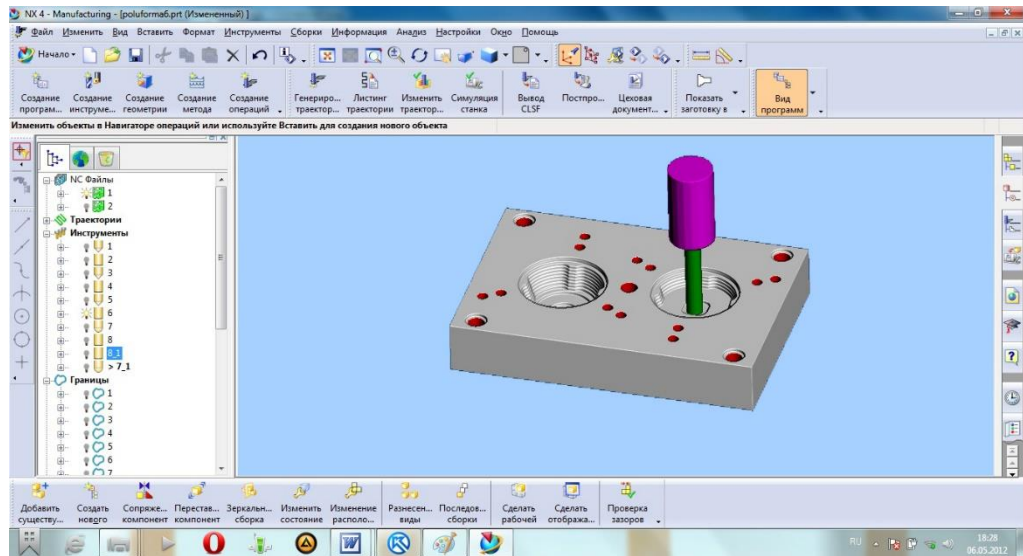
Чернова обробка внутрішньої поверхні
